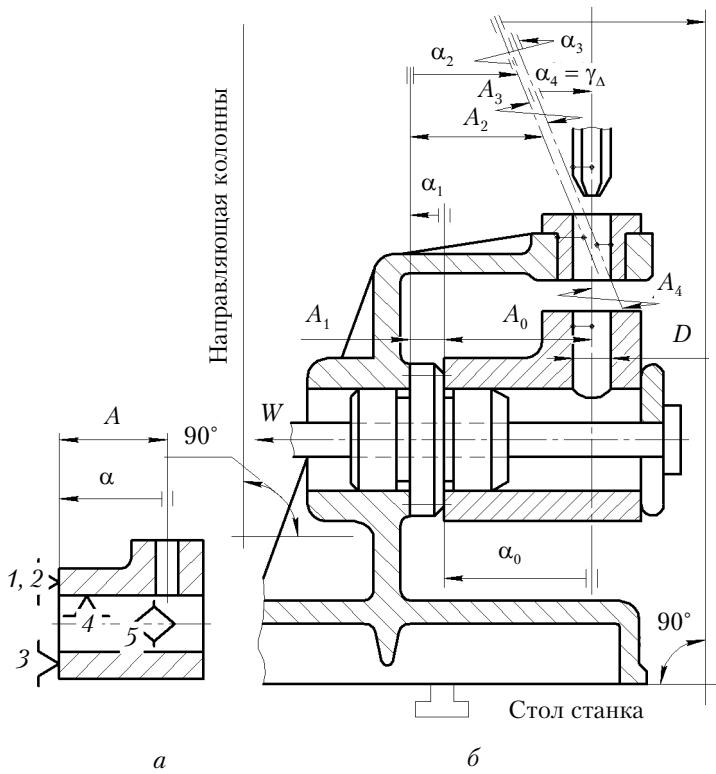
Схема сверлильного приспособления с размерным анализом
